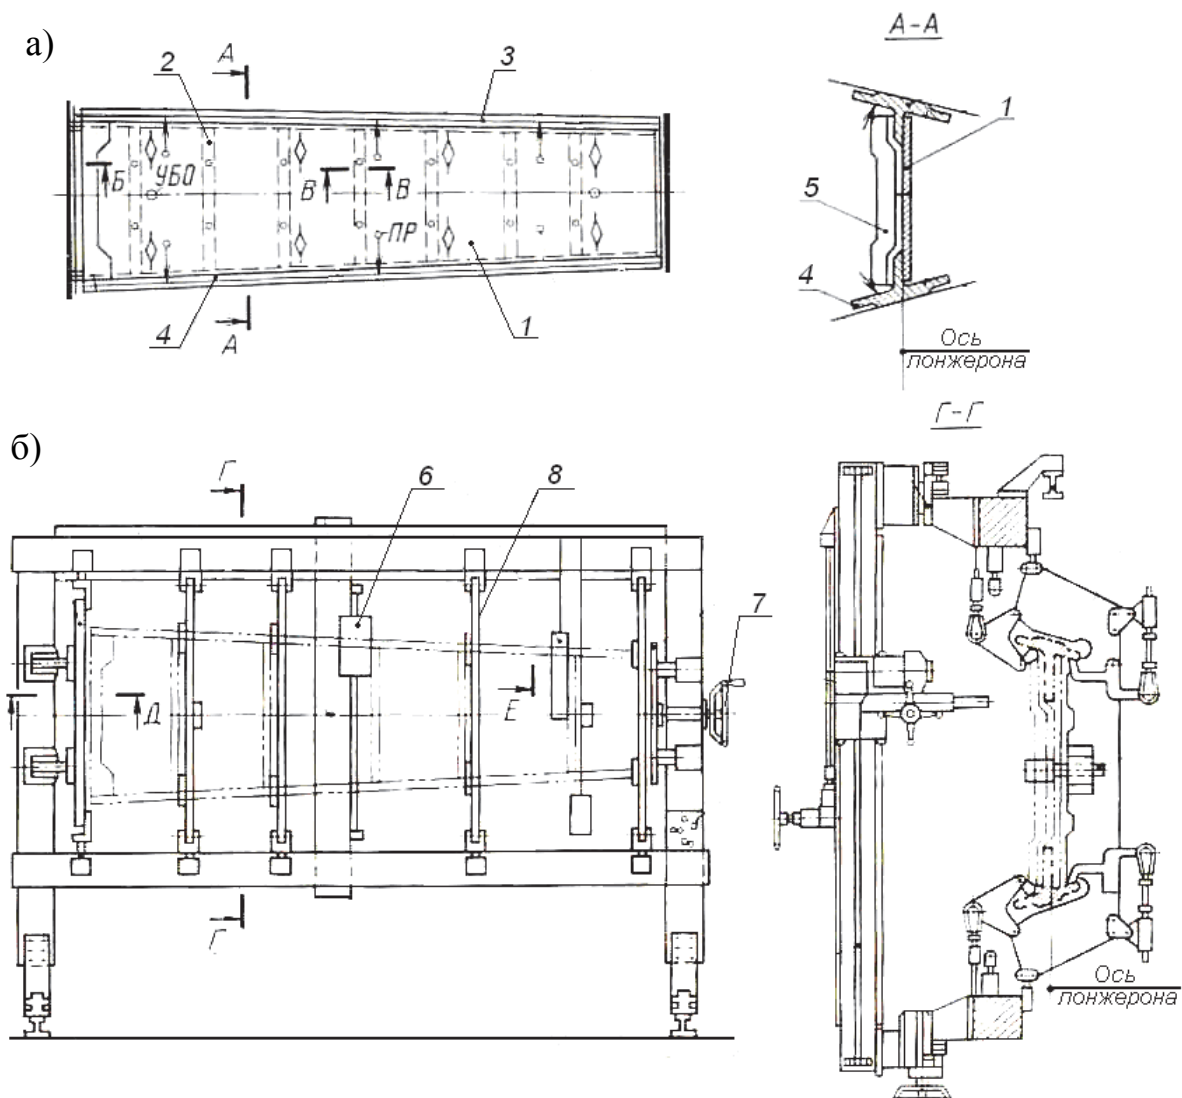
Элементы лонжерона и сборочного приспособления:
